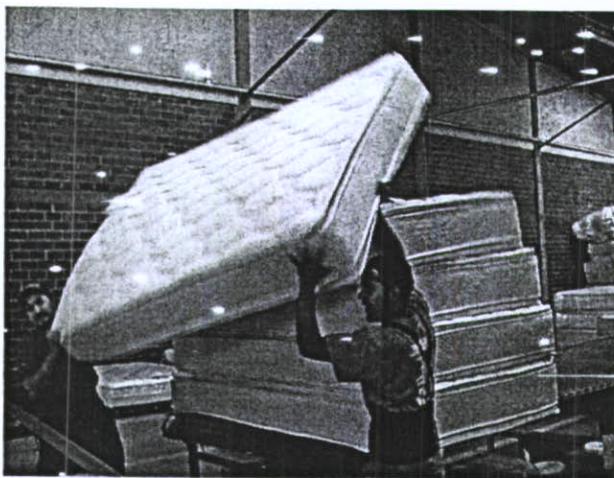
Antes los trabajadores bajaban el colchón para embolsarlo.
